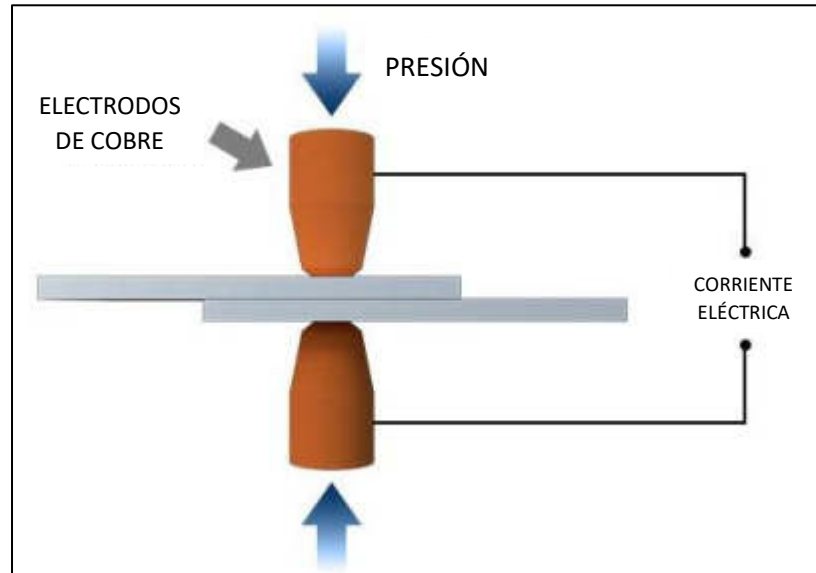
Esquema de la soldadura por puntos por resistencia [5]
